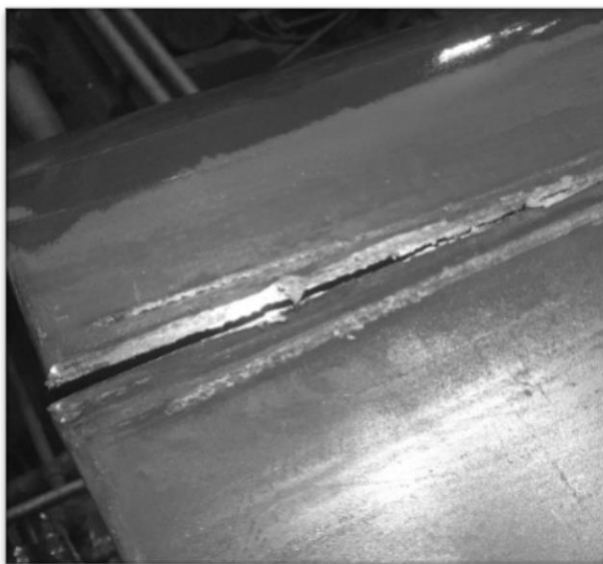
Extremo de tubería soldada por SAW con falta de fusión en ascenso
